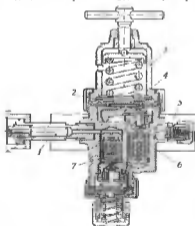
Двухступенчатый кислородный редуктор БКД-50: 1 — штуцер входа газа; 2 — мембрана; 3 — стальная пружина; 4 — рычаг; 5 — предохранительный клапан; 6 — регулирующий клапан второй ступени; 7 — регулирующий клапан первой ступени
